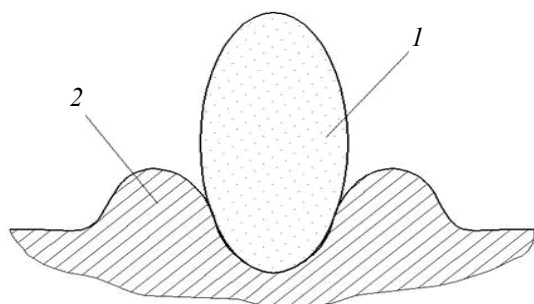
Образование наплыва металла вдоль следа обработки: 1 – абразивное зерно; 2 – наплывы металла вдоль следа обработки
